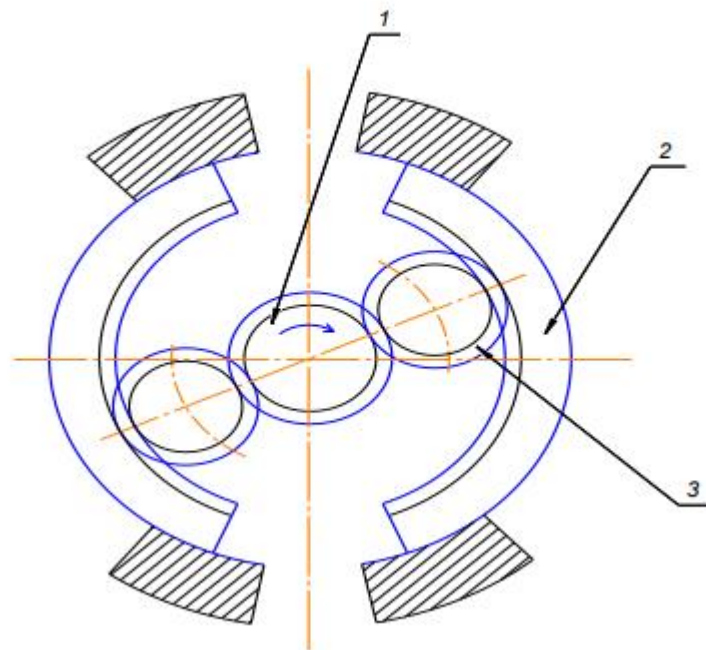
а – Планетарний процес накатування: 1 – нерухомі сегменти; 2 - обертовий нарізевий ролик; 3 – деталі, що обробляються
